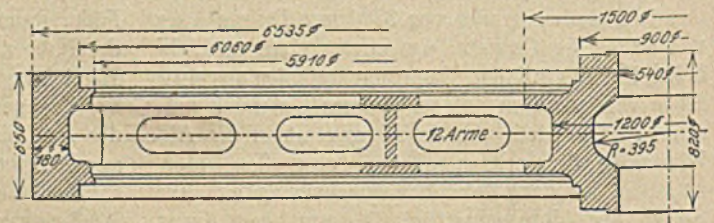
Induktorrad Abb. 42 mit richtig konstruierten Speichen.
